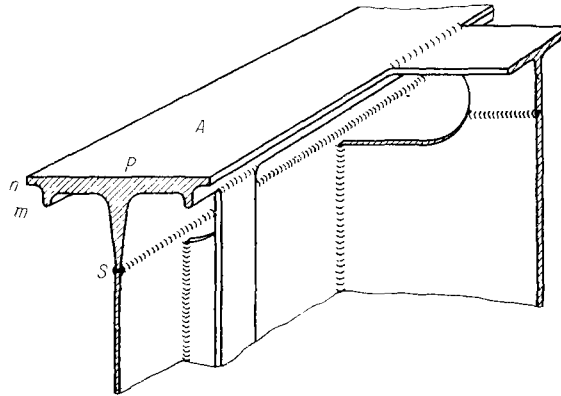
Конструкция сварных балок из алюминиевых сплавов
